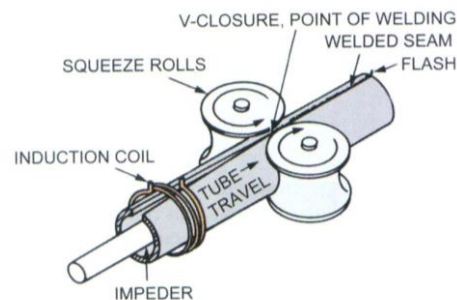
Ejemplo de Soldadura HRFW
